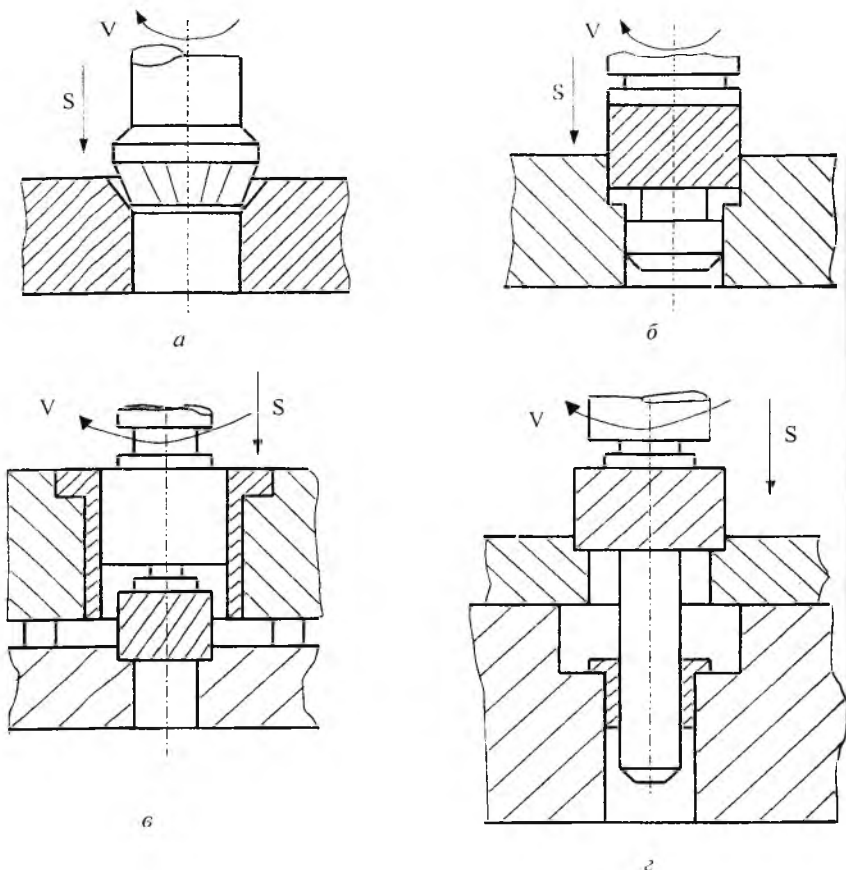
Схема зенкерования отверстий: *а* – обработка фасок в отверстиях под конус – зенковка; *б* – обработка фасок в отверстиях под цилиндр – цековка; *в* – верхнее заднее направление зенкера в кондукторной втулке; *г* – нижнее переднее направление зенкеров в кондукторной втулке
